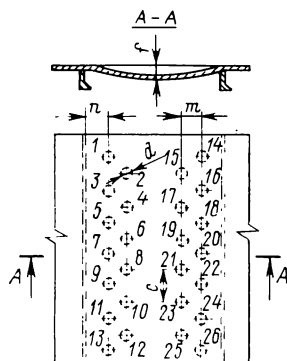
Схема нагрева при выполнении правки тонколистовой обшивки.
